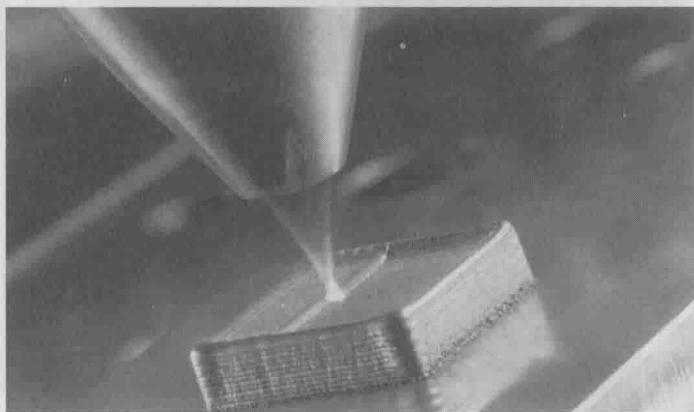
增材制造:在工件上激光沉积焊接
